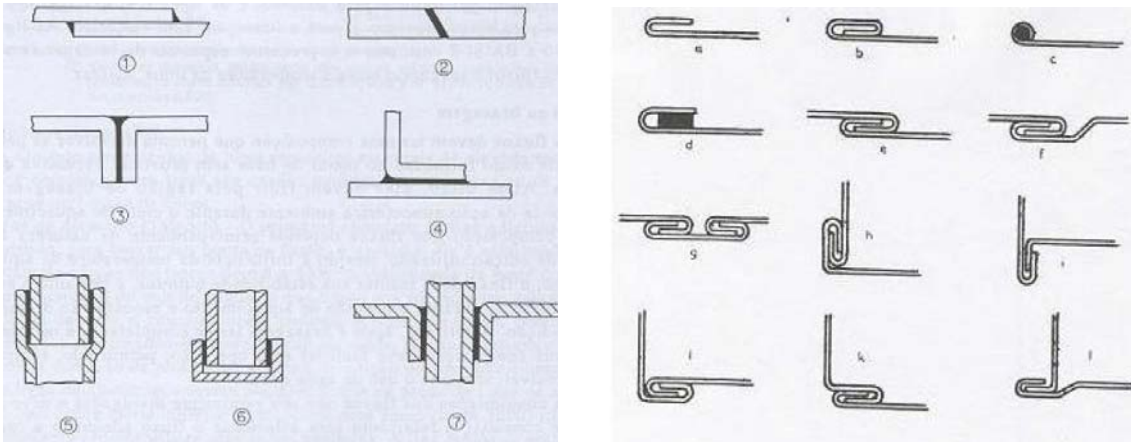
Juntas para brazagem (esquerda) e juntas para solda fraca (direita) [30].
